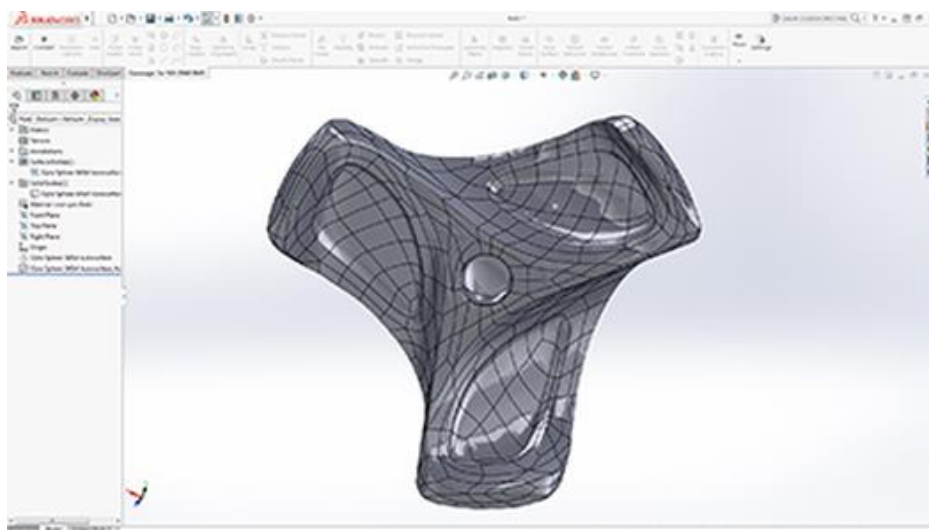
Peça dissenyada amb plug-in per a impressió 3D en SolidWorks; Font: [5]
